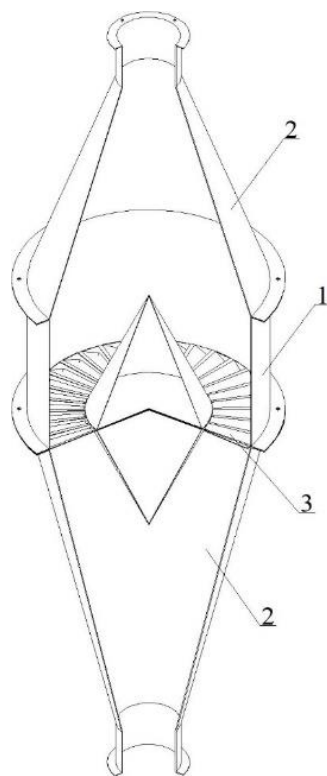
Схема аппарата с цилиндрической рабочей камерой:
